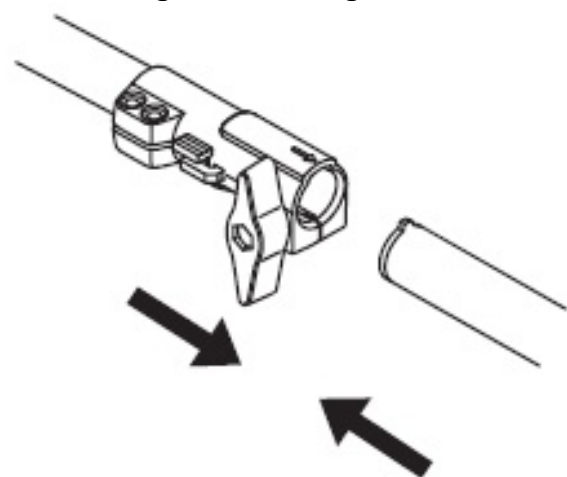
Зчленування верхньої та нижньої труб вала
